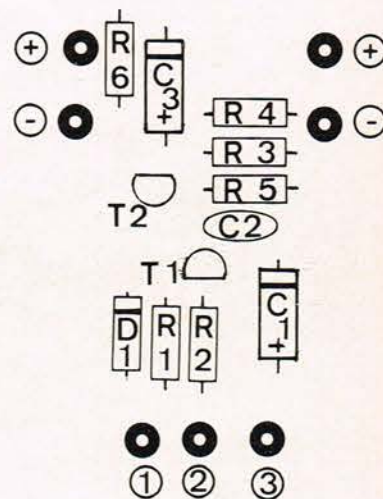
Sireneprint. Printet set fra komponentsiden.
